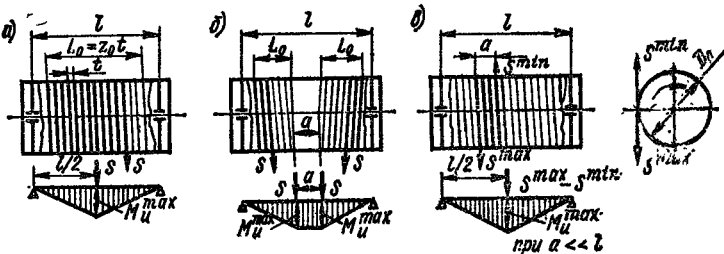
Расчетные схемы барабанов: а — с креплением одного конца каната; б — с креплением двух концов каната; в — с фрикционными витками
